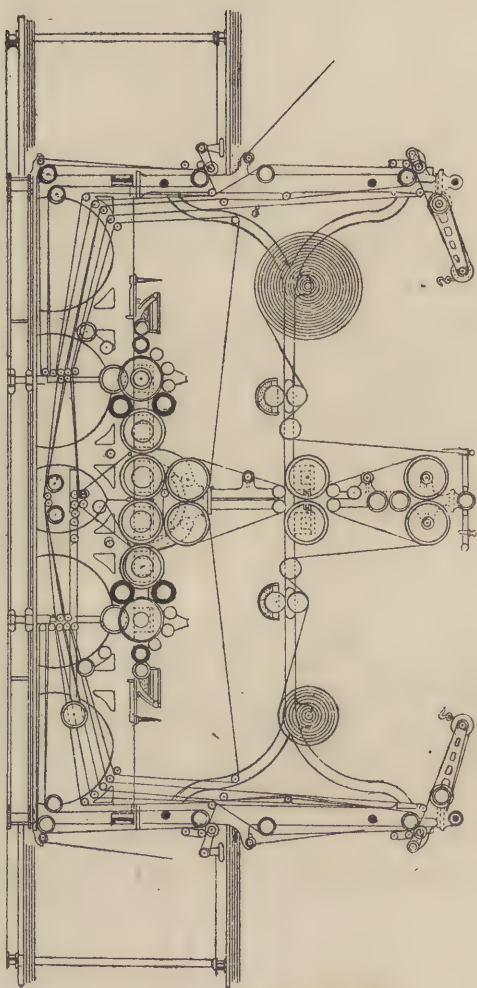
MACHINE CYLINDRIQUE A PAPIER CONTINU,
